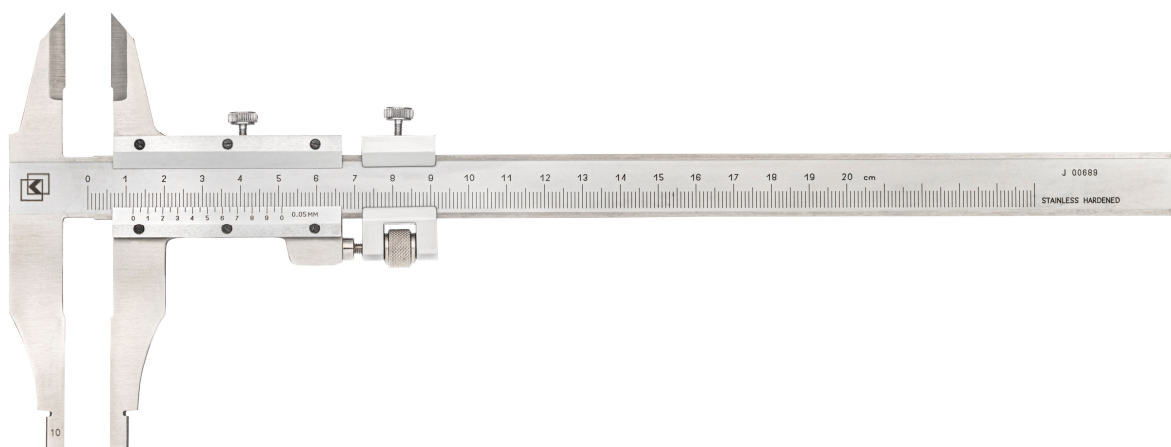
Общий вид штангенциркулей ШЦ-II
